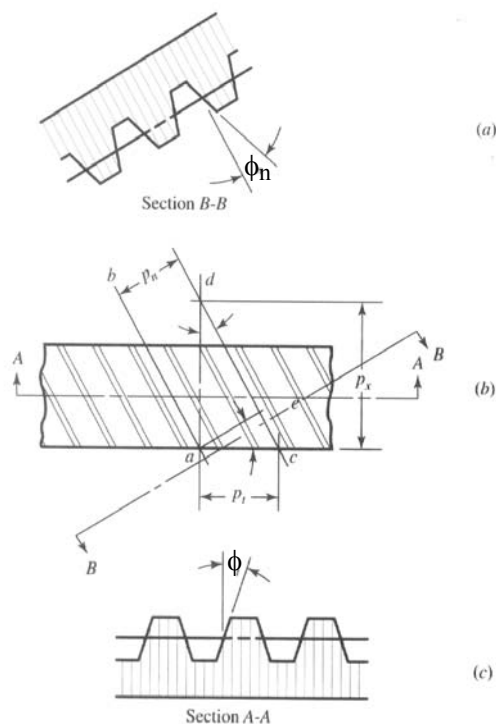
Nomenclatura e definições em engrenagens cilíndricas helicoidais
